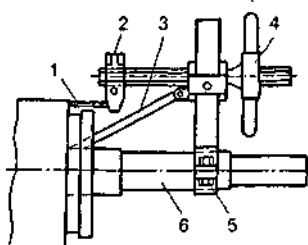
Приспособление для извлечения стержней из пазов ротора
